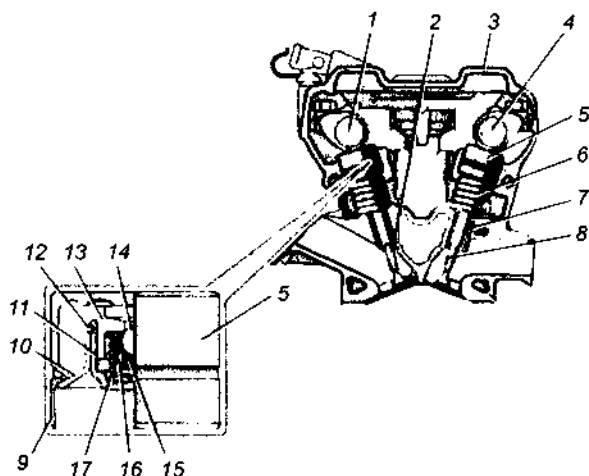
Газораспределительный механизм ЗМЗ-4062: 1, 4 — распределительные валы впускных и выпускных клапанов соответственно; 2 — впускной клапан; 3 — крышка клапанов; 5 — гидравлический толкатель клапана; 6 — наружная пружина клапана; 7 — направляющая втулка клапана; 8 — выпускной клапан; 9 — корпус толкателя; 10 — направляющая втулка; 11 — корпус компенсатора; 12 — стопорное кольцо; 13 — поршень компенсатора; 14 — шариковый клапан; 15 — пружина шарикового клапана; 16 — корпус шарикового клапана; 17 — разжимная пружина
